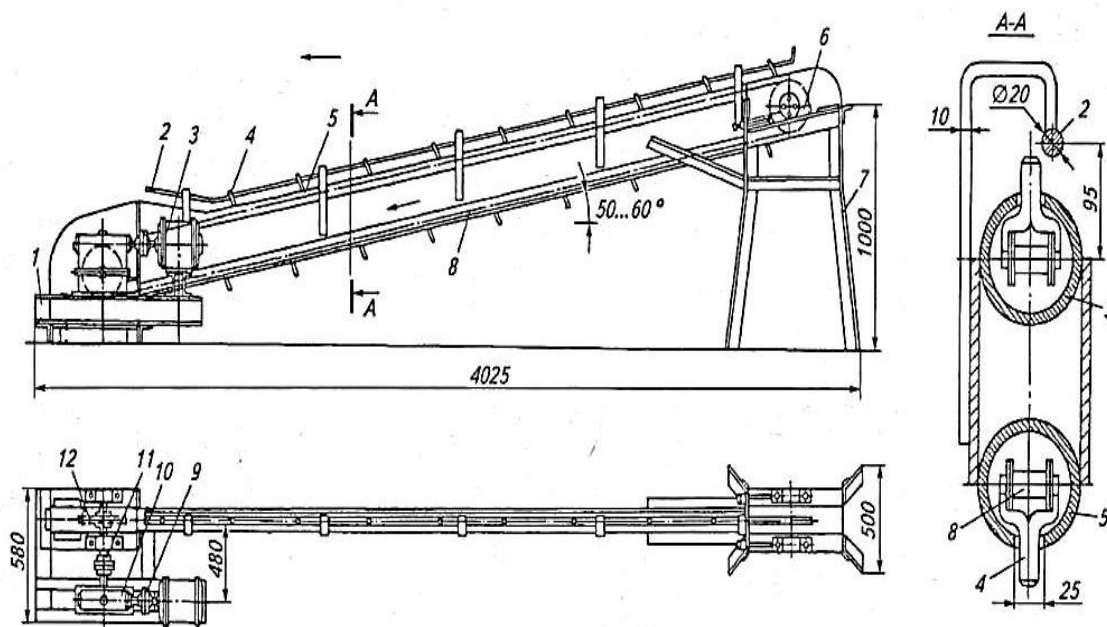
Двухконвейерная установка для съемки шкур с туш мелкого рогатого скота: 1 – станина; 2 – ограничитель; 3 – электродвигатель; 4 – палец; 5 – трубы-направляющие; 6 – натяжная станция; 7 – каркас; 8 – тяговая цепь; 9, 11 – муфты; 10 – червячный редуктор; 12 – ведущая звездочка
